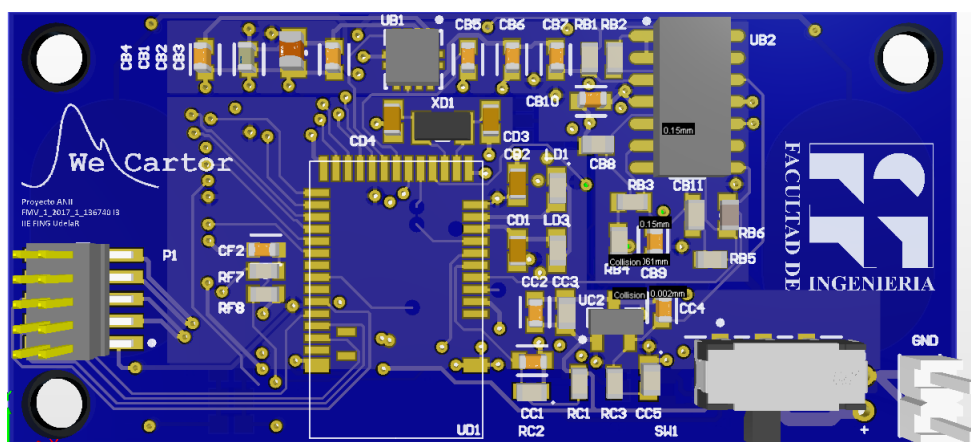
Vista 3D desde TOP generada utilizando Altium Designer de la PCB Test.
